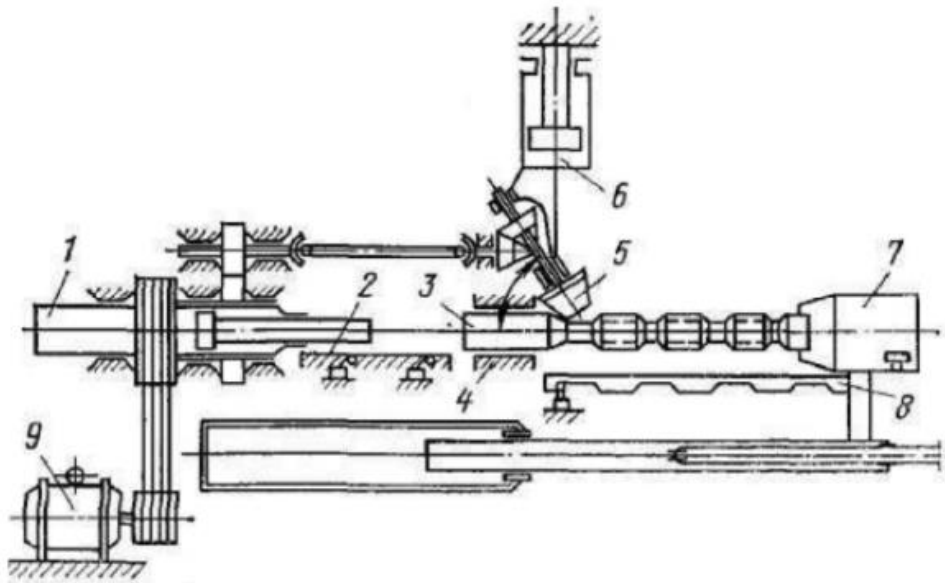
Тривалковий стан 100 гарячої прокатки круглих періодичних профілів: 1 - пневматичний штовхач; 2 - прийомний жолоб; 3 - заготовка; 4 - проходка; 5 - прокатний валок; 6 - гідравлічний циліндр натискного механізму; 7 - затискний патрон; 8 - копіювальна лінійка; 9 - привід валків
